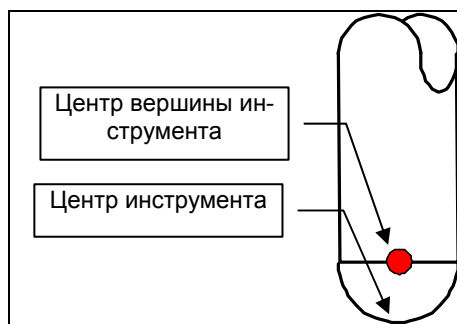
(f) Вершина концевой сферической фрезы
